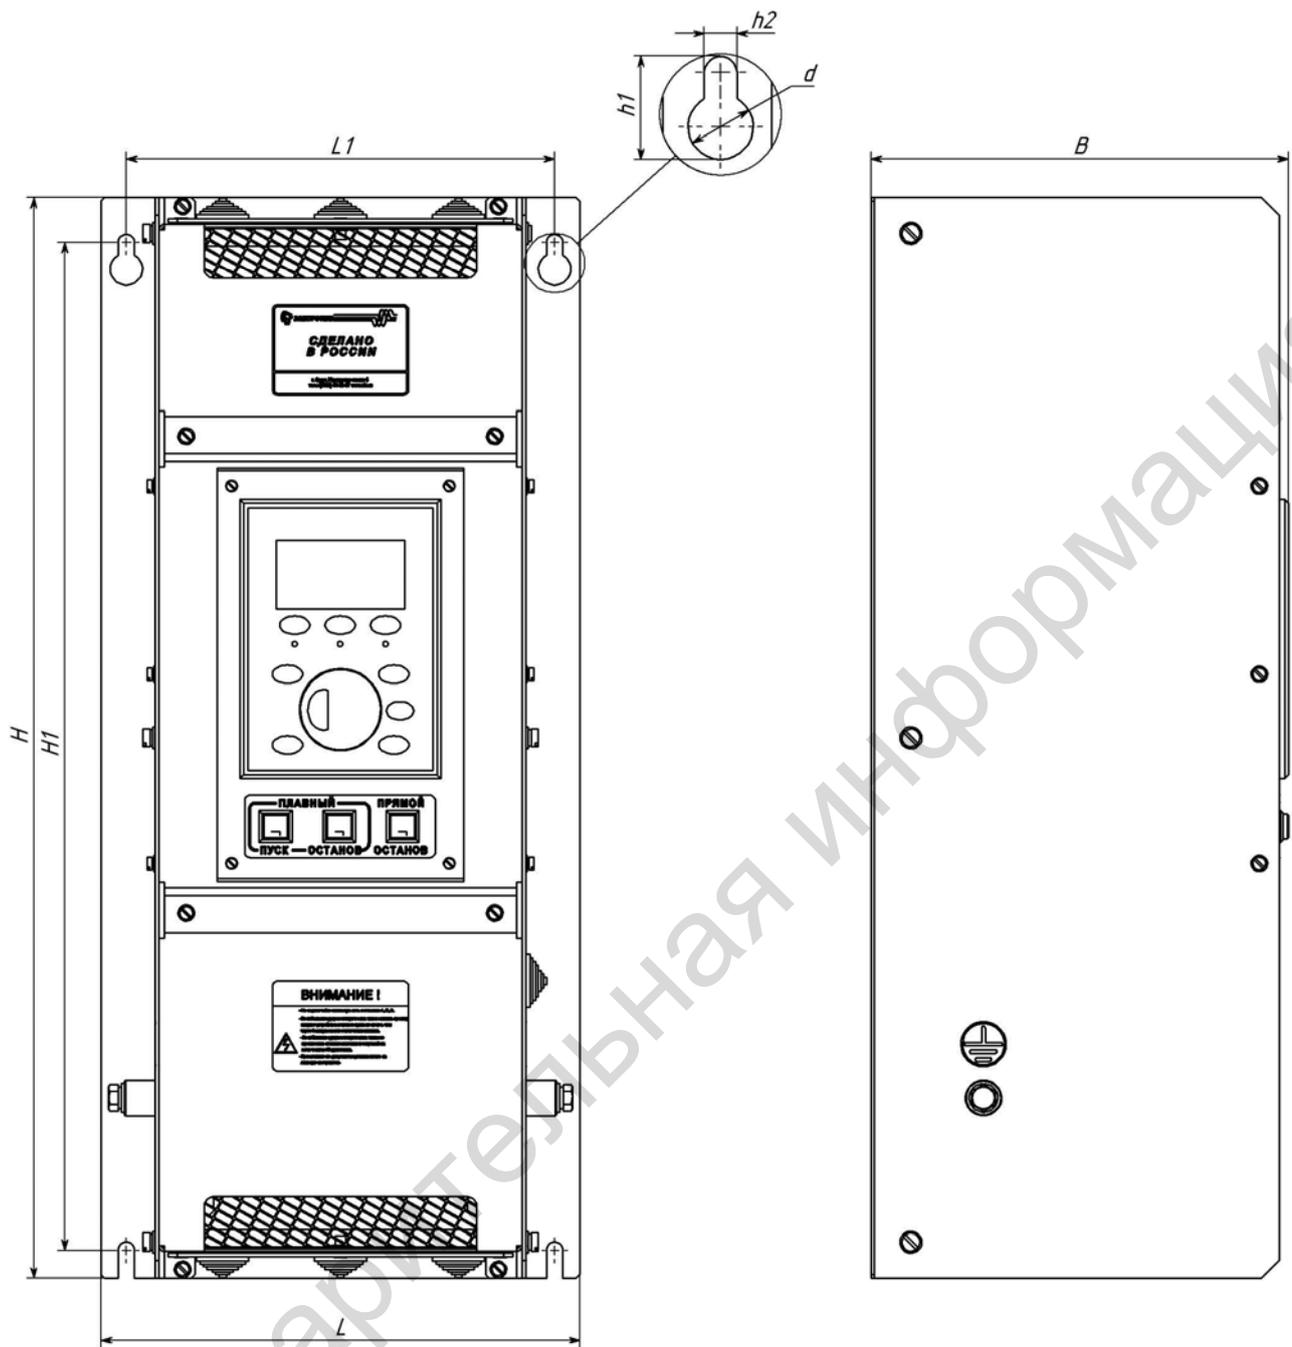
Габаритные и установочные размеры УПП 45-132 кВт
